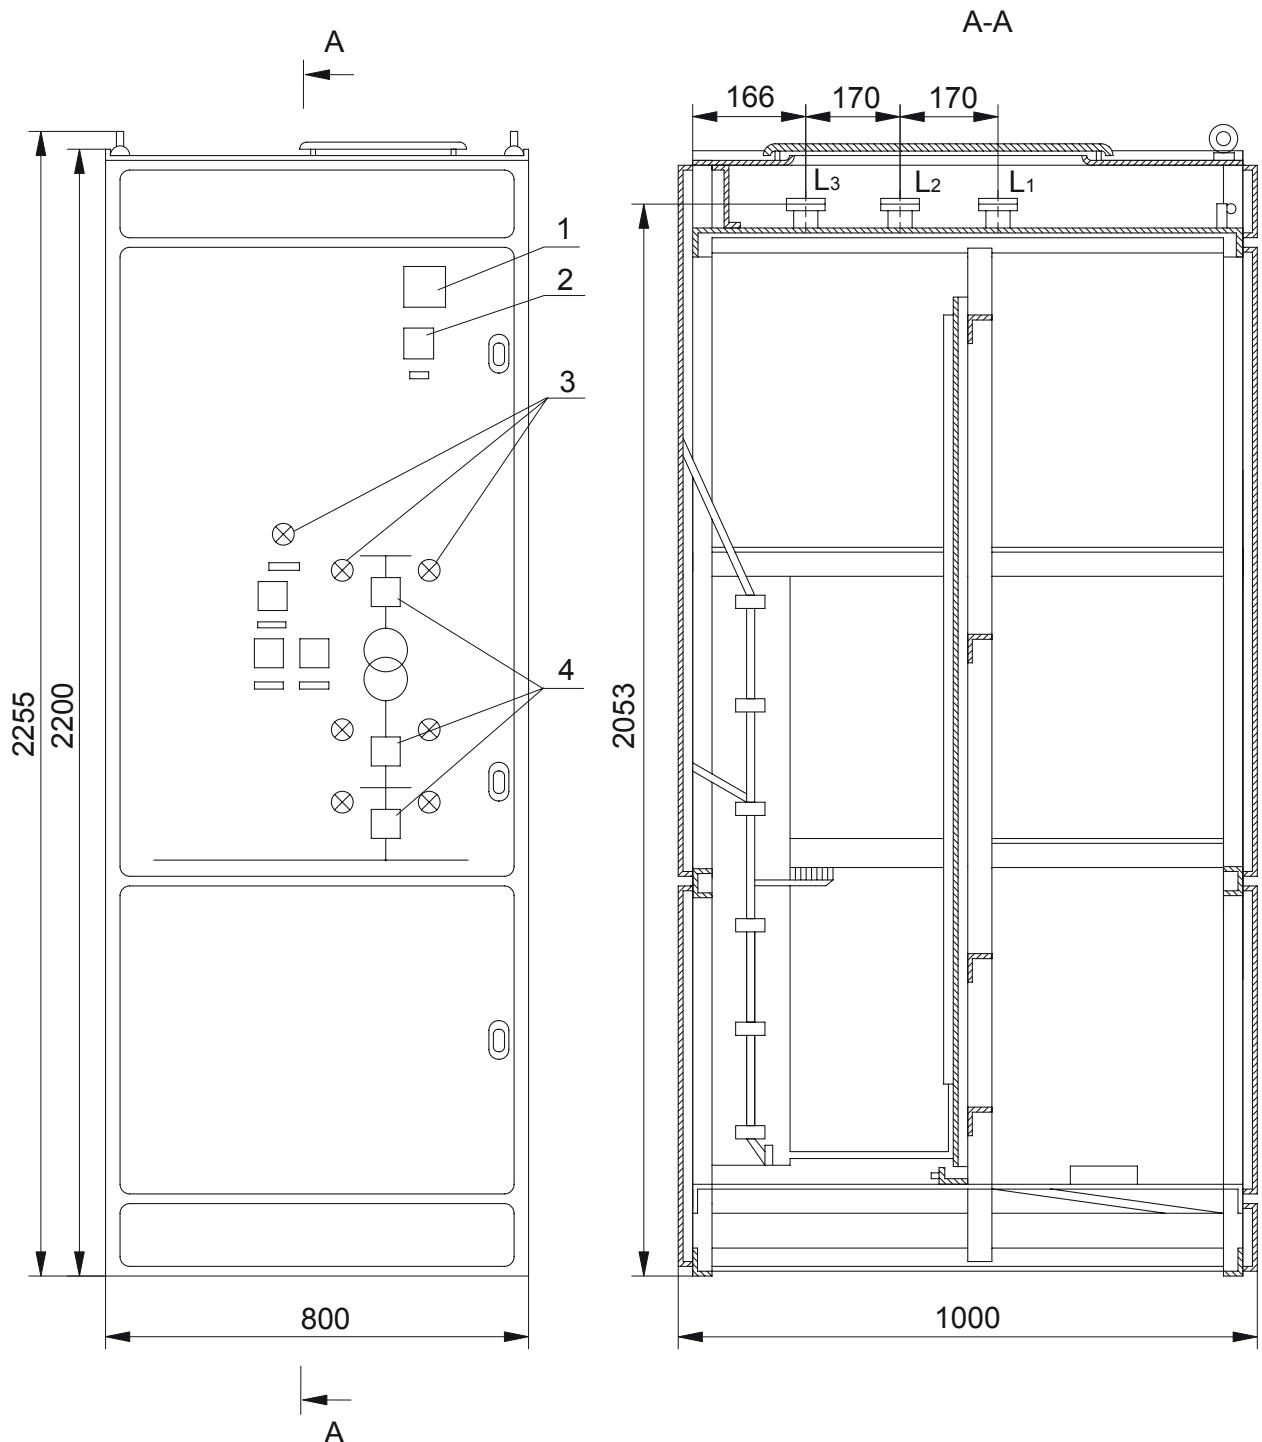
Габаритные размеры шкафов 7ШН-70 (5ШН-70):
